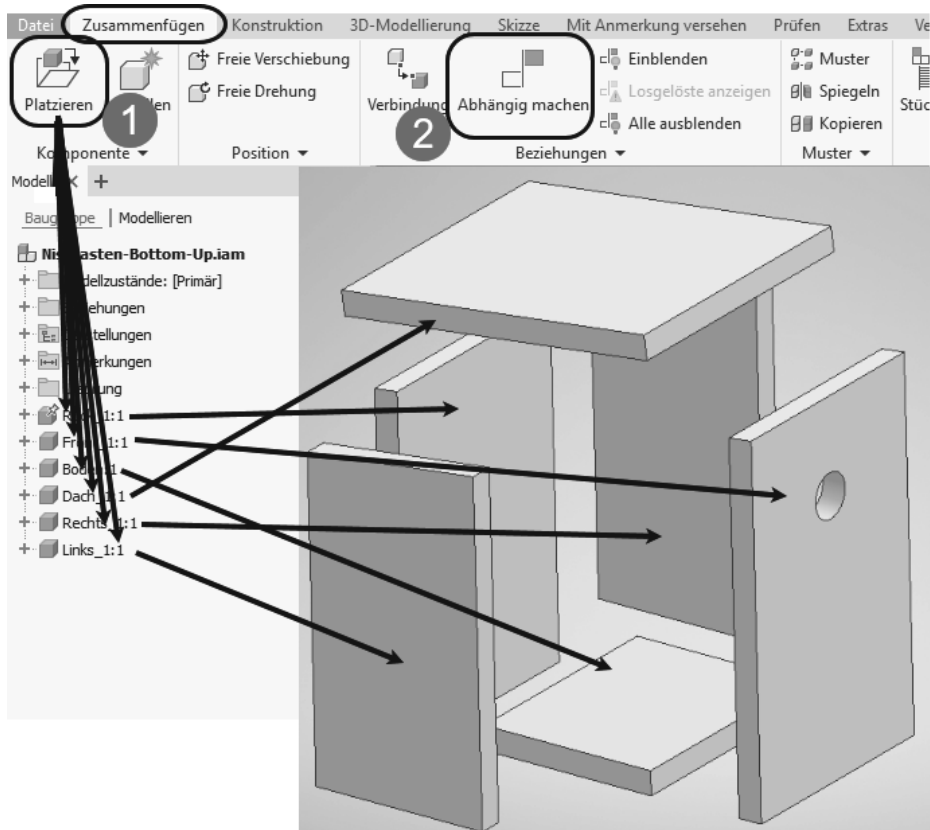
Baugruppe nach dem Bottom-Up-Verfahren zusammenbauen
